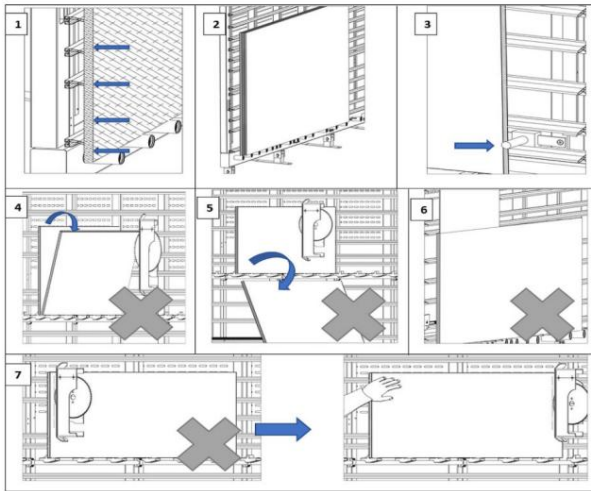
Posicionamiento de la pieza de trabajo en la sierra de paneles.
